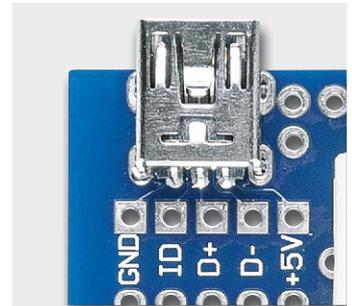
Die Pin-Bezeichnungen der USB-Buchse sind auf der Platine aufgedruckt.
